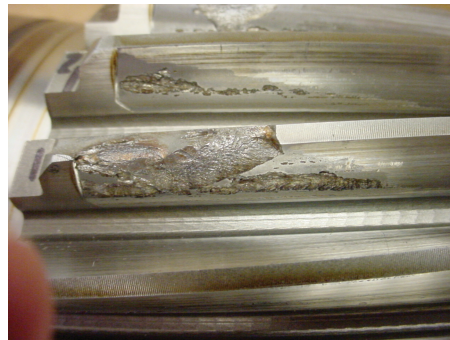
Défaut d'engrenage par pitting [42].
